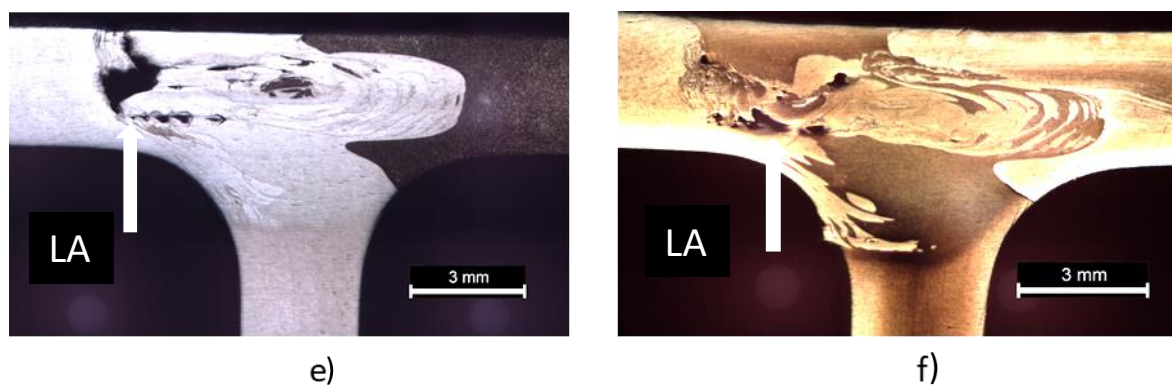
Macrografias das soldaduras: e) 562-240-M (Keller modificado); f) 265-240-M (Weck).
